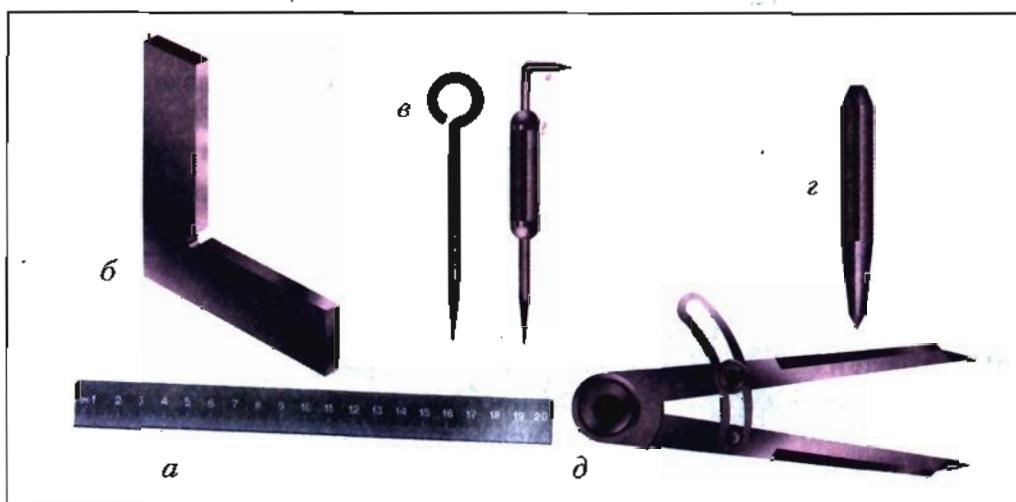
Разметочные инструменты: *а* – линейка; *б* – угольник; *в* – чертилки; *г* – кернер; *д* – разметочный циркуль
